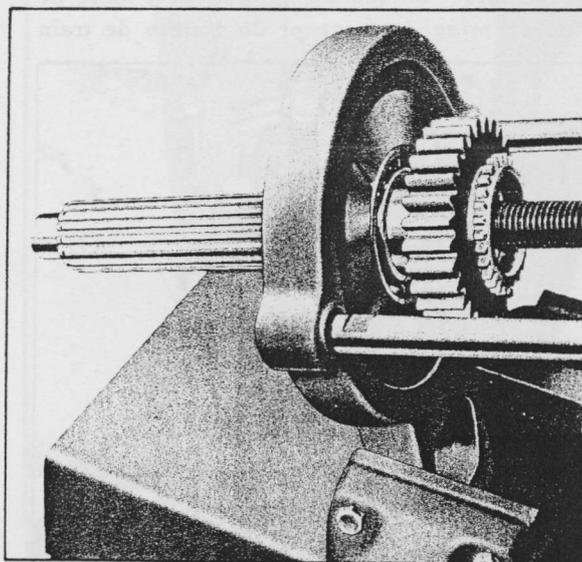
= Repose du Roulement a billes d'Arbre supérieur Principal
